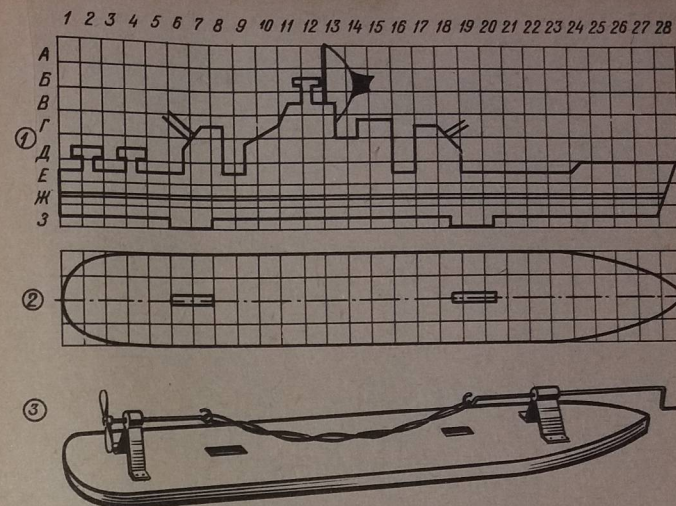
Модель корабля противолодочной обороны: 1—силуэт корабля; 2—вид сверху на днище корпуса; 3—наглядное изображение установки резинового
